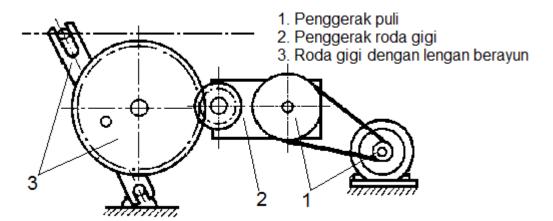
Komponen-komponen mesin shaping horizontal
